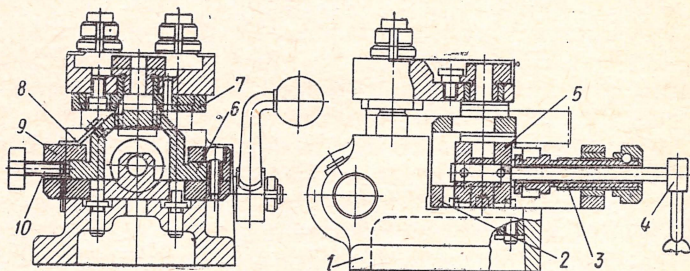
Наладочный скальчатый кондуктор для сверления деталей типа вилок
